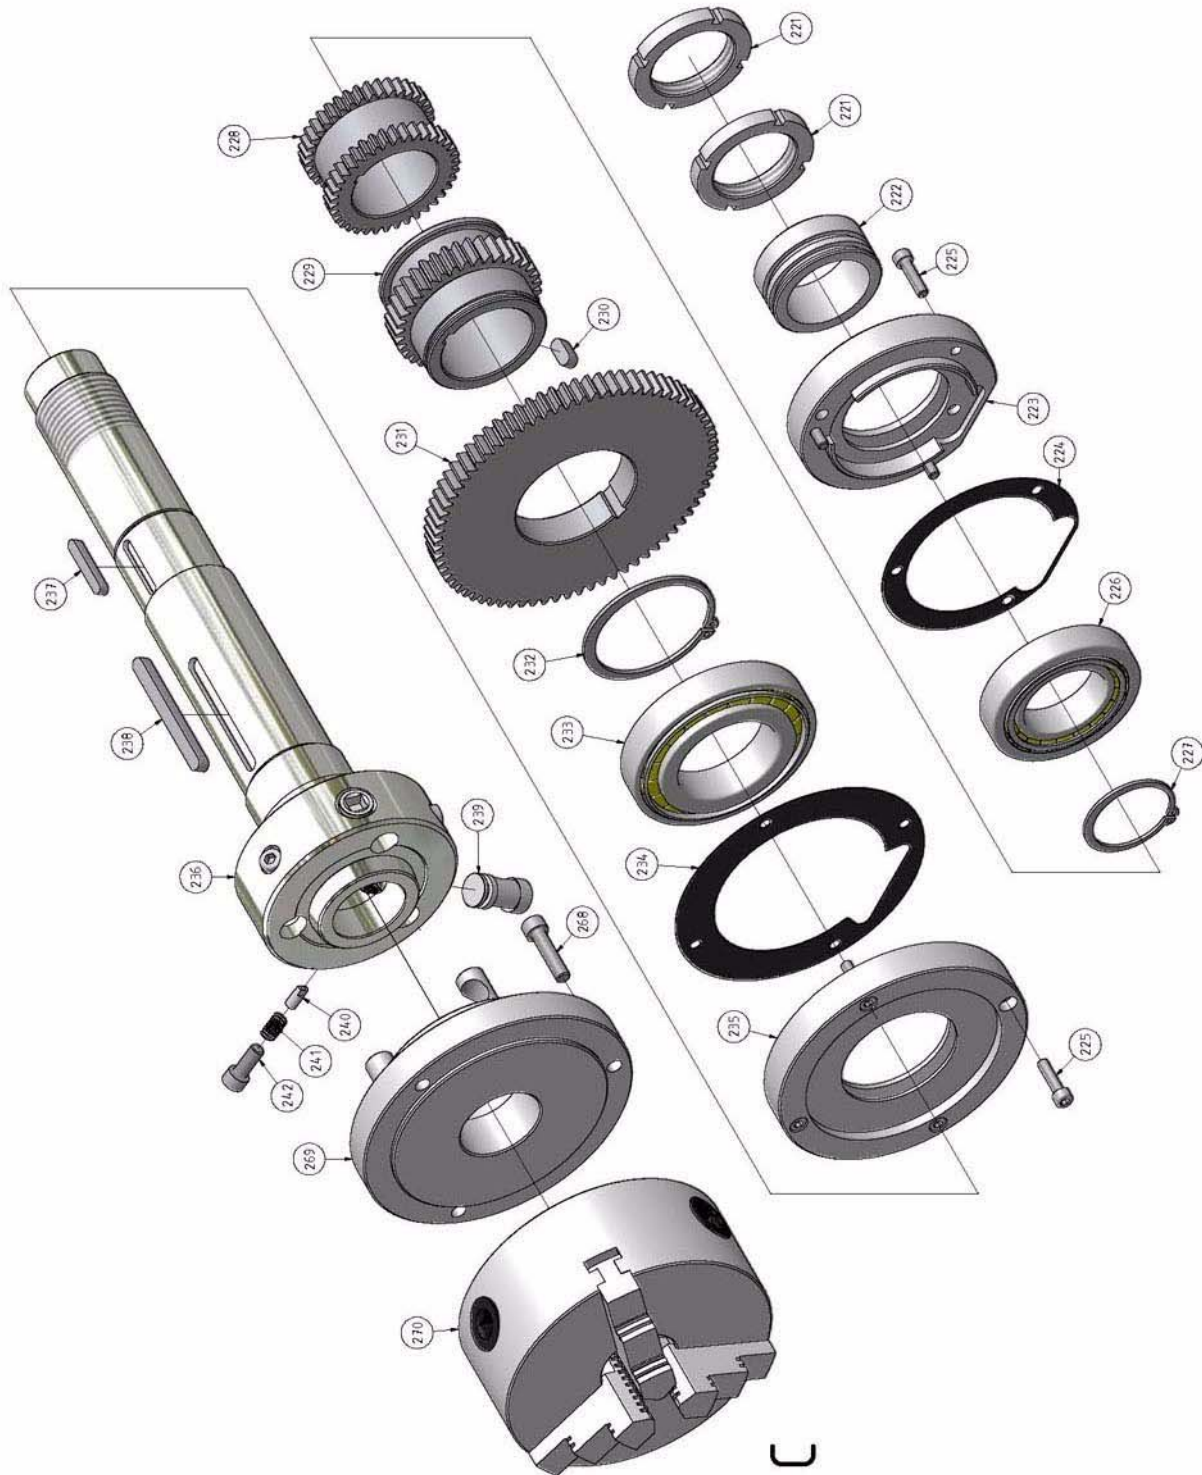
Getriebe Spindelstock 4-6 - Headstock gear 4-6
